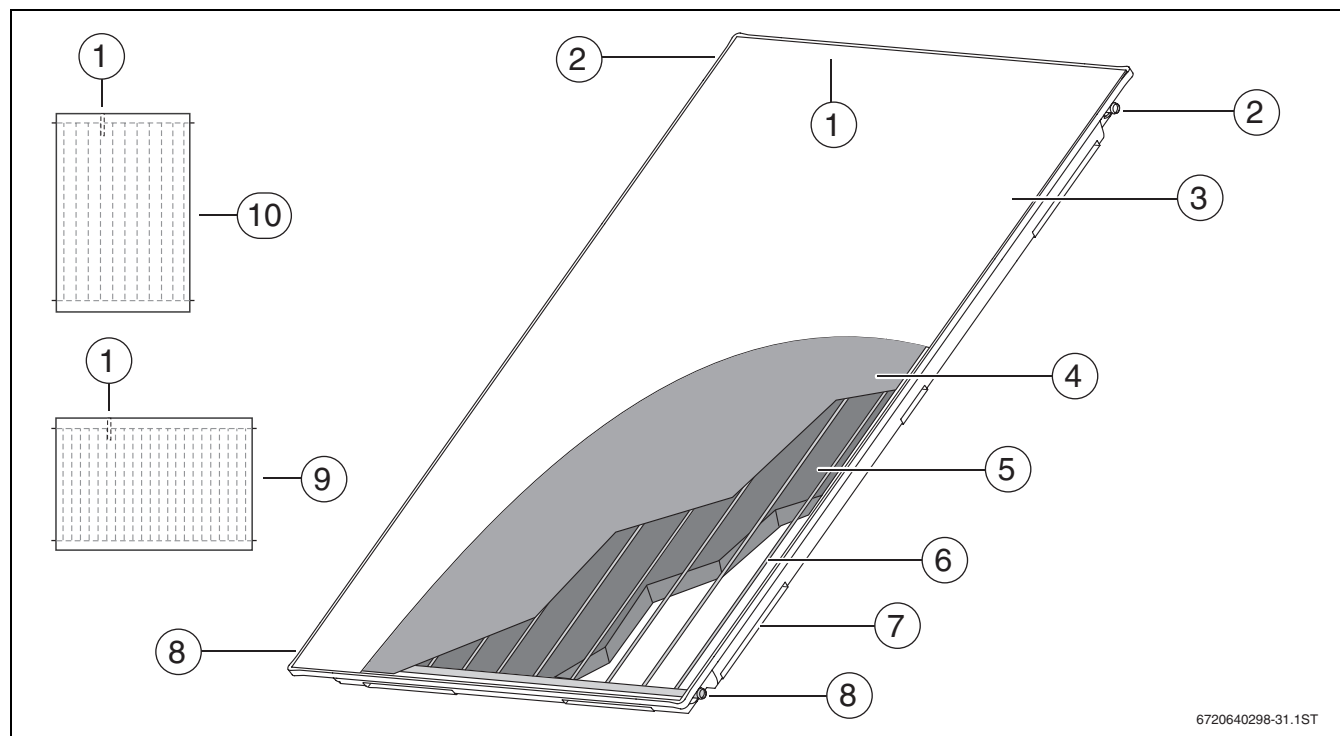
Tipo di collettori verticale con rappresentazione in sezione
